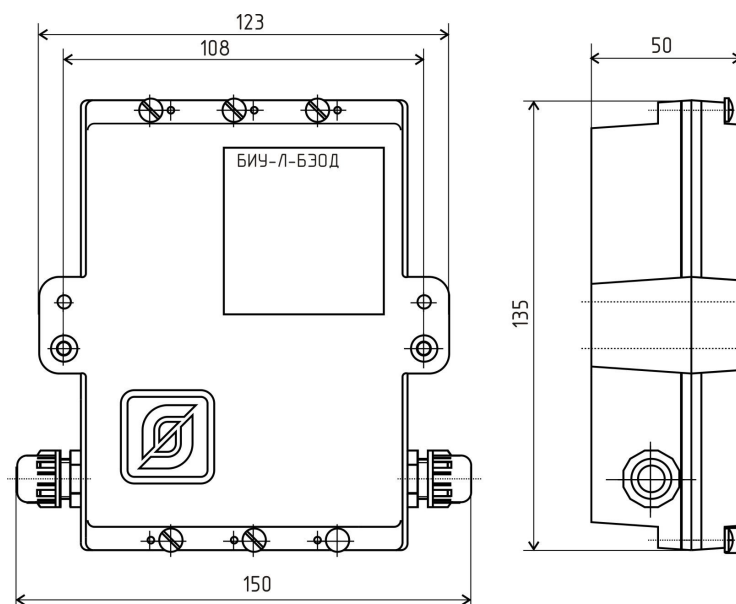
Габаритные размеры БИУ-Л-БЭОД
